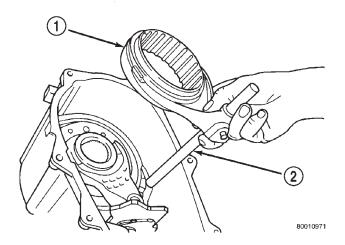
Desmontaje de la horquilla y el manguito de modo
